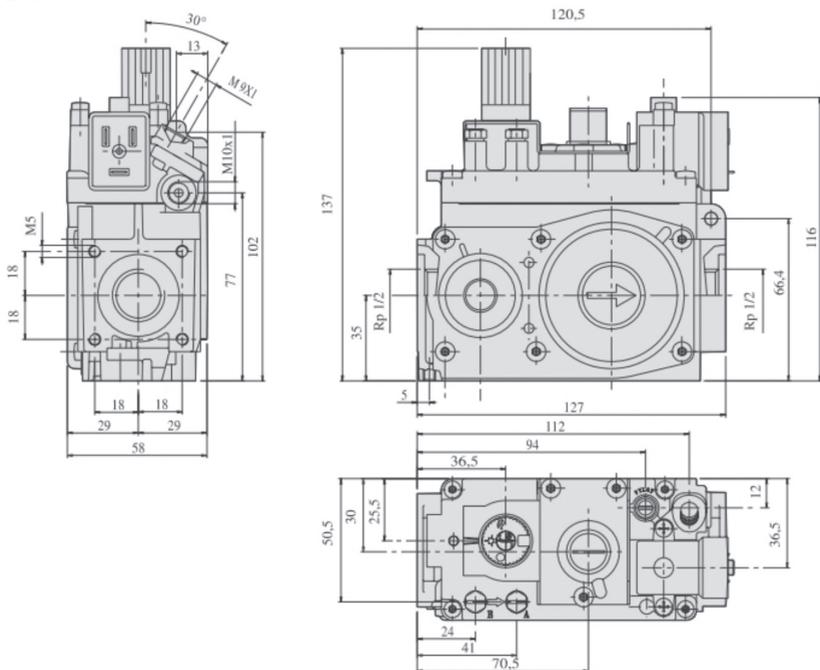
Габаритные и присоединительные размеры клапана SIT NOVA 820
